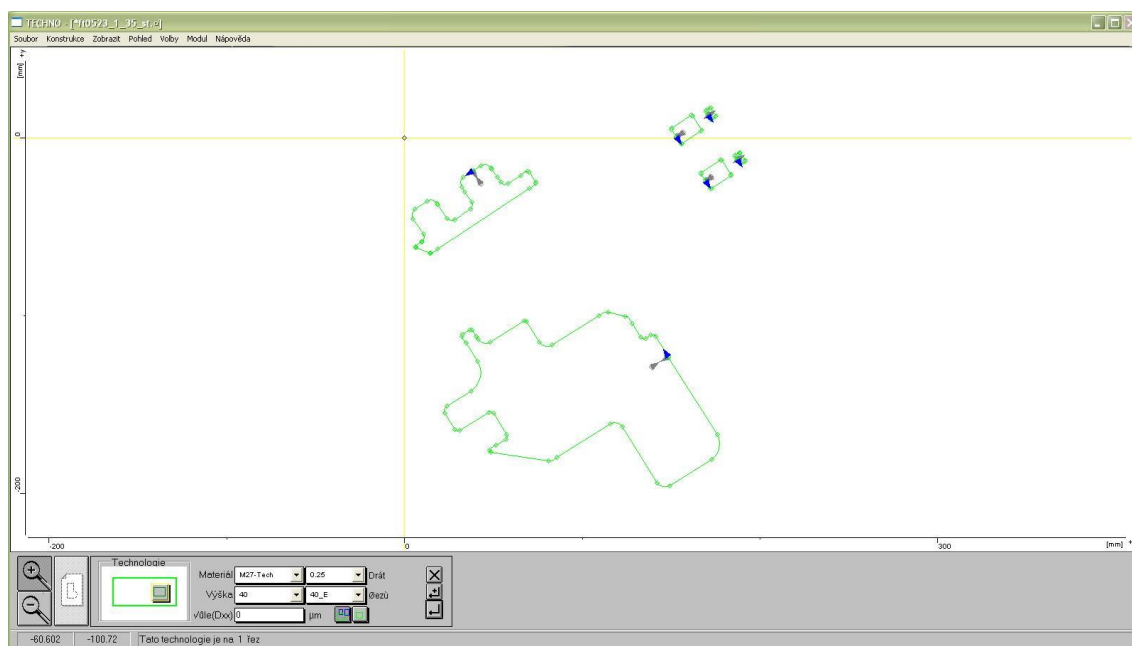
Zobrazenie súčiastky v systéme WIRECUT v module CAD
